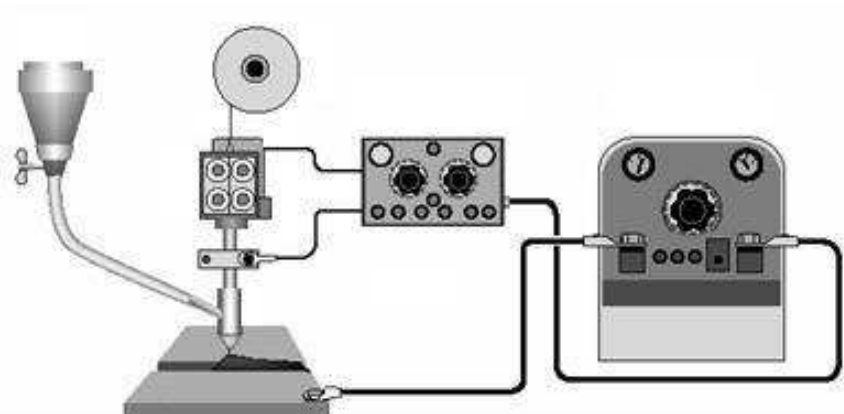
Diagrama esquemático del equipo de soldadura SAW
